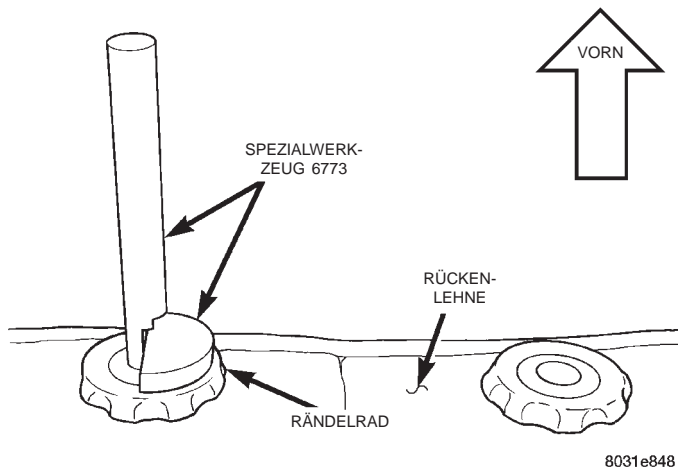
Spezialwerkzeug zum Ausbau von Kopfstützenaufnahmen
